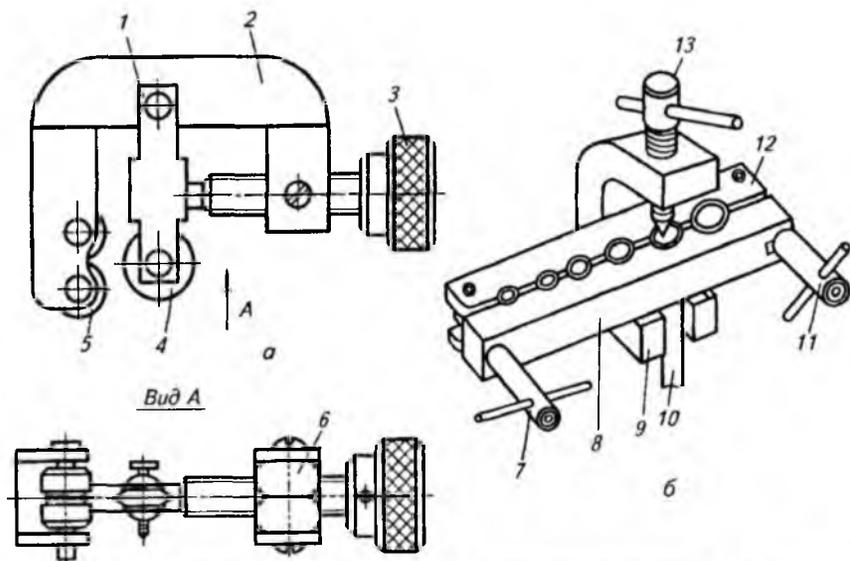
Схема трубореза (а) и приспособление для развальцовки трубок (б):
